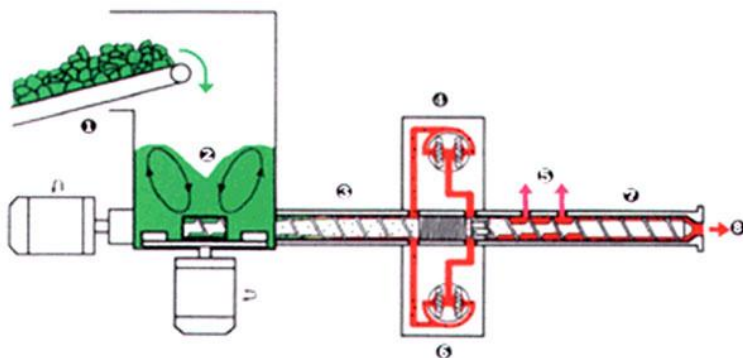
Установка для изготовления нити из переработанного ПЭТ-пластика [3]
